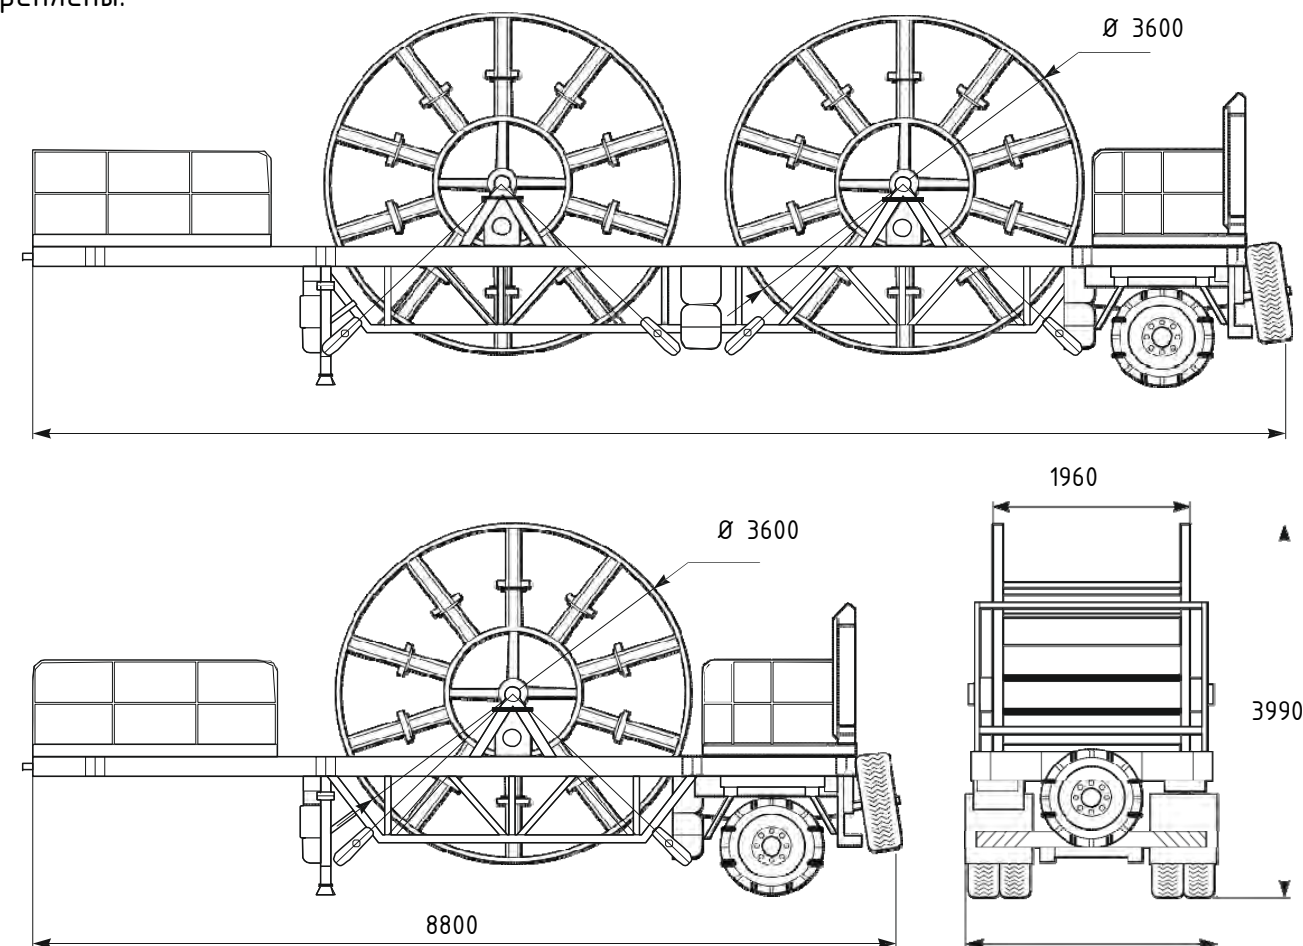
Внешний вид и габариты прицепов для транспортирования барабанов
